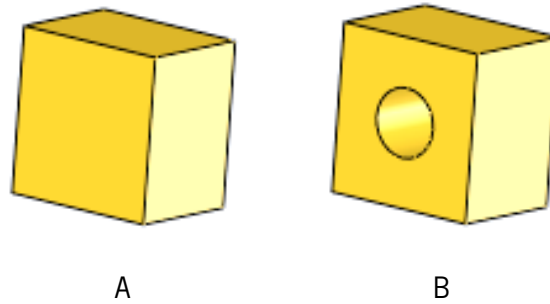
Fase de fabrico do pé (superfície de contacto)
